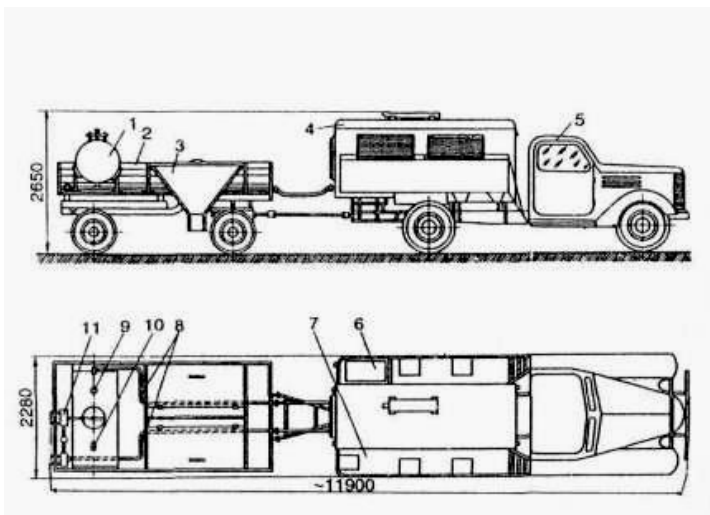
Самоходный агрегат для ремонта трещин:
